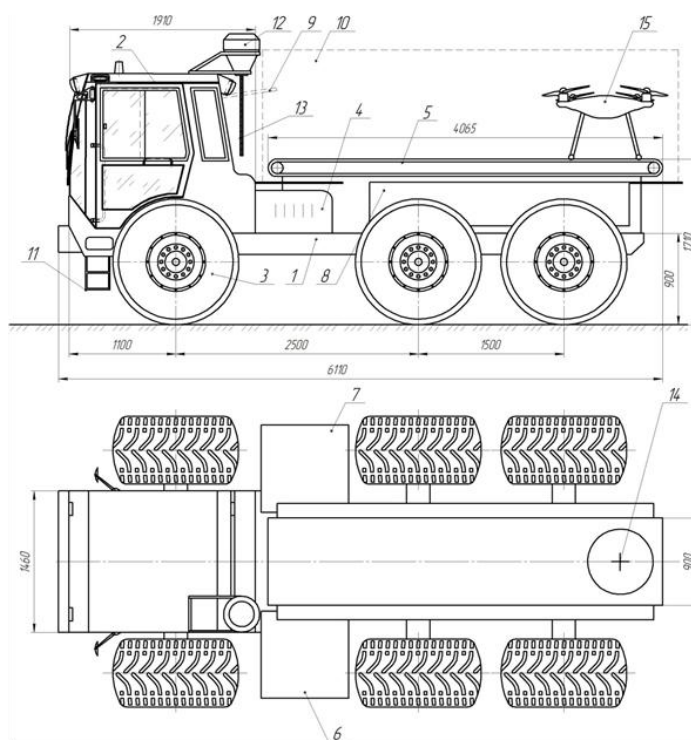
Внешний вид мобильного средства, оборудованного шинами сверхнизкого давления: 1 – рама; 2 – кабина; 3 – шина сверхнизкого давления; 4 – силовая установка; 5 – подвижный взлетно-посадочный стол; 6, 7 – площадки для обслуживания дронов; 8 – емкость для приманки; 9 – откидное окно; 10 – съемный тент; 11 – лестница; 12 – бак для приманки; 13 – система подачи приманки; 14 – место взлета и посадки БПЛА; 15 – БПЛА
